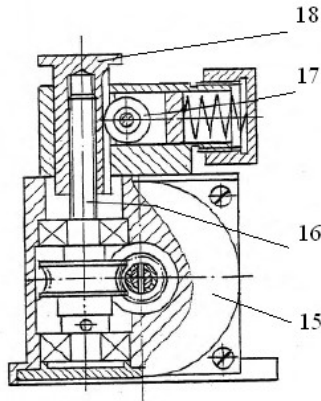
Конструкция устройства автоматической подачи кристалла алмаза:
